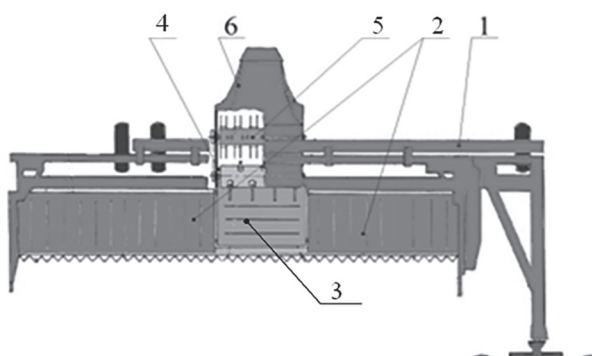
Прицепной жатвенный агрегат на базе прицепной валковой жатки для измельчения очесанного стеблестоя, его разбрасывания по полю, или погрузки в транспортное средство:
